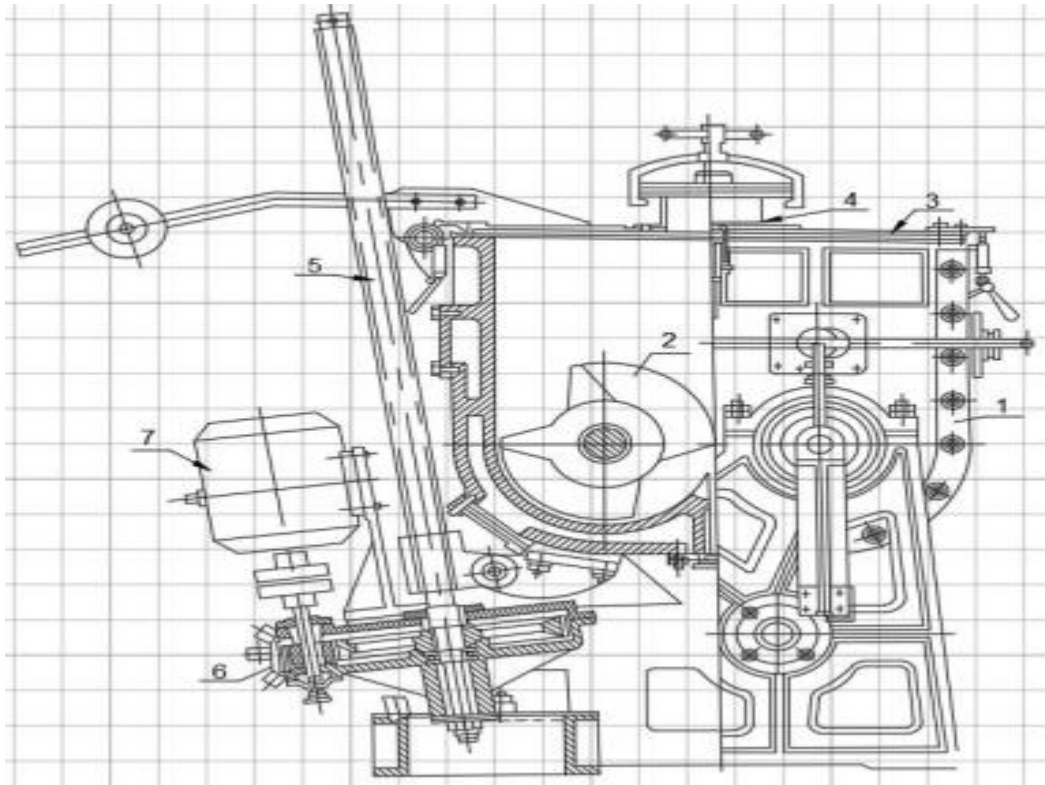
Змішувач СМ-400: 1 - корпус змішувача; 2 - лопаті; 3 - відкидна кришка; 4 - завантажувальний отвір; 5 — гвинт для нахилу та підйому корпусу; 6 - електропередача; 7 - електродвигун; 8 - гайка корпусу змішувача
